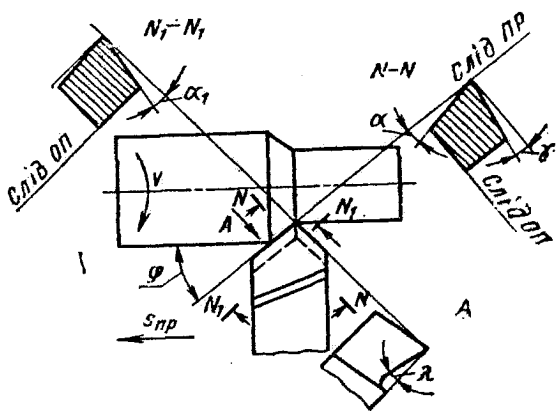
Кути токарного різця у статичній системі координат
